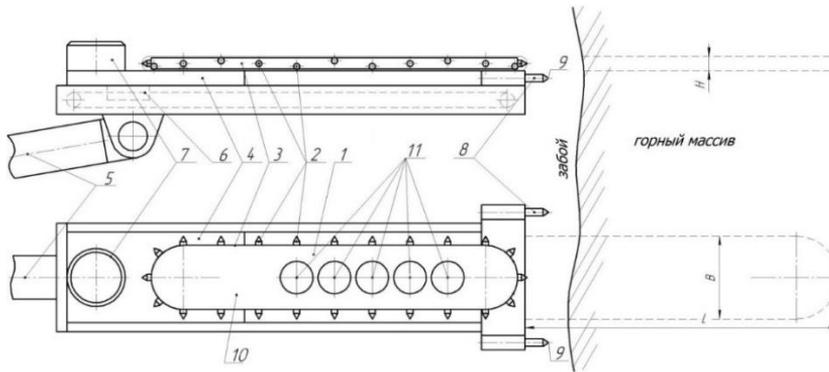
Схема исполнительного органа агрегата для проходческо-очистных работ:
